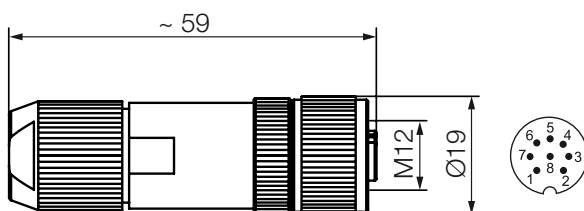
Steckverbinder BCC M478-0000-10-000-43x834-000
